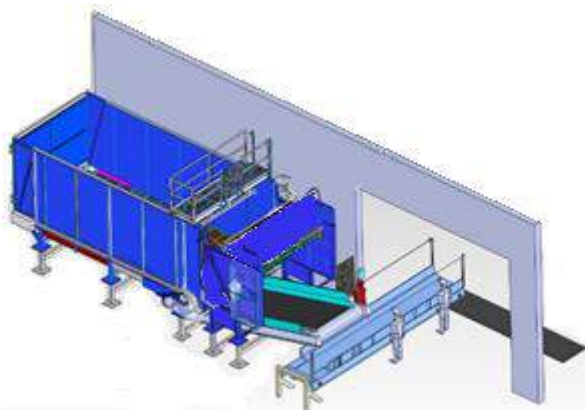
Общий вид разрывателя пакетов DKZ-B50M3 фирмы "Netmus"
